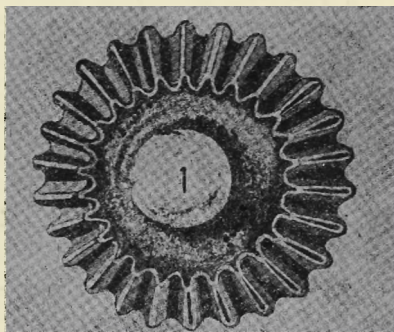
Шестерня из русской платины; отлита в 1859 г. Сен-Клер-Девиллем, Дебрэ и Якоби.
